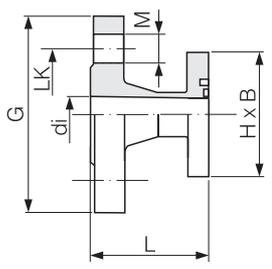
Abmessungen Frontansicht Messaufnehmer DN 2...25
